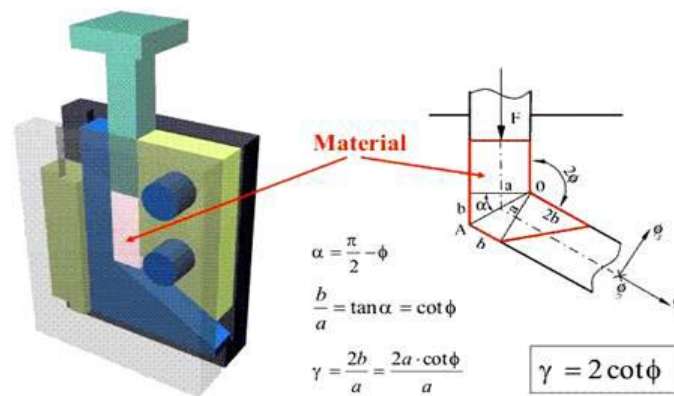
La technique du tube coudé (ECA – Equal Channel Angular Pressing).
